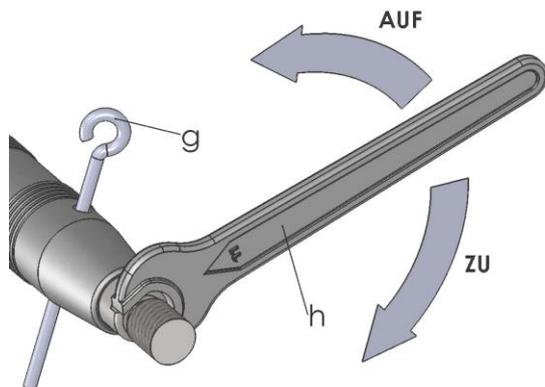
Werkzeugwechsel Spannzange ZG 1 / ZG 1a
